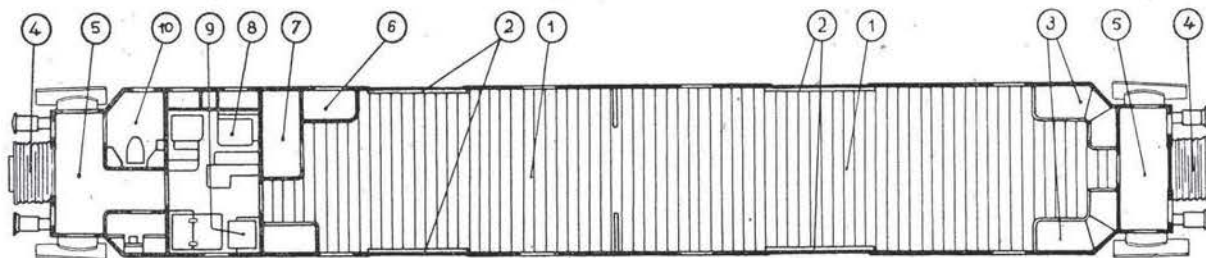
Grundriß des Packwagens Pw 4ü-36. 1 Grundriß, 2 Ladeöffnungen (Schiebetüren), 3 Regale für kleinere Gepäckstücke, 4 geschlossener Übergang, 5 Vorraum, 6 Hundeabteil, 7 Schränke für Kleingeräte, 8 Zugführersitz und Arbeitsplatz, 9 Ladeschaffnersitz, 10 Abort mit Waschgelegenheit
